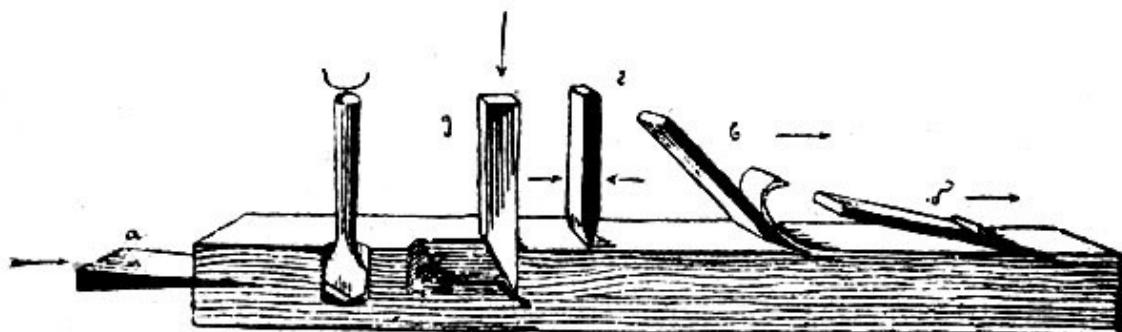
а – раскалывание; б – резание; в – строгание; г – скобление; д – долбление; е – сверление
